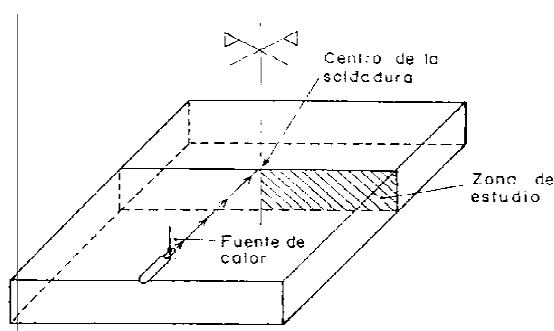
Esquema de la fuente de calor durante el proceso de soldadura por arco [1].
